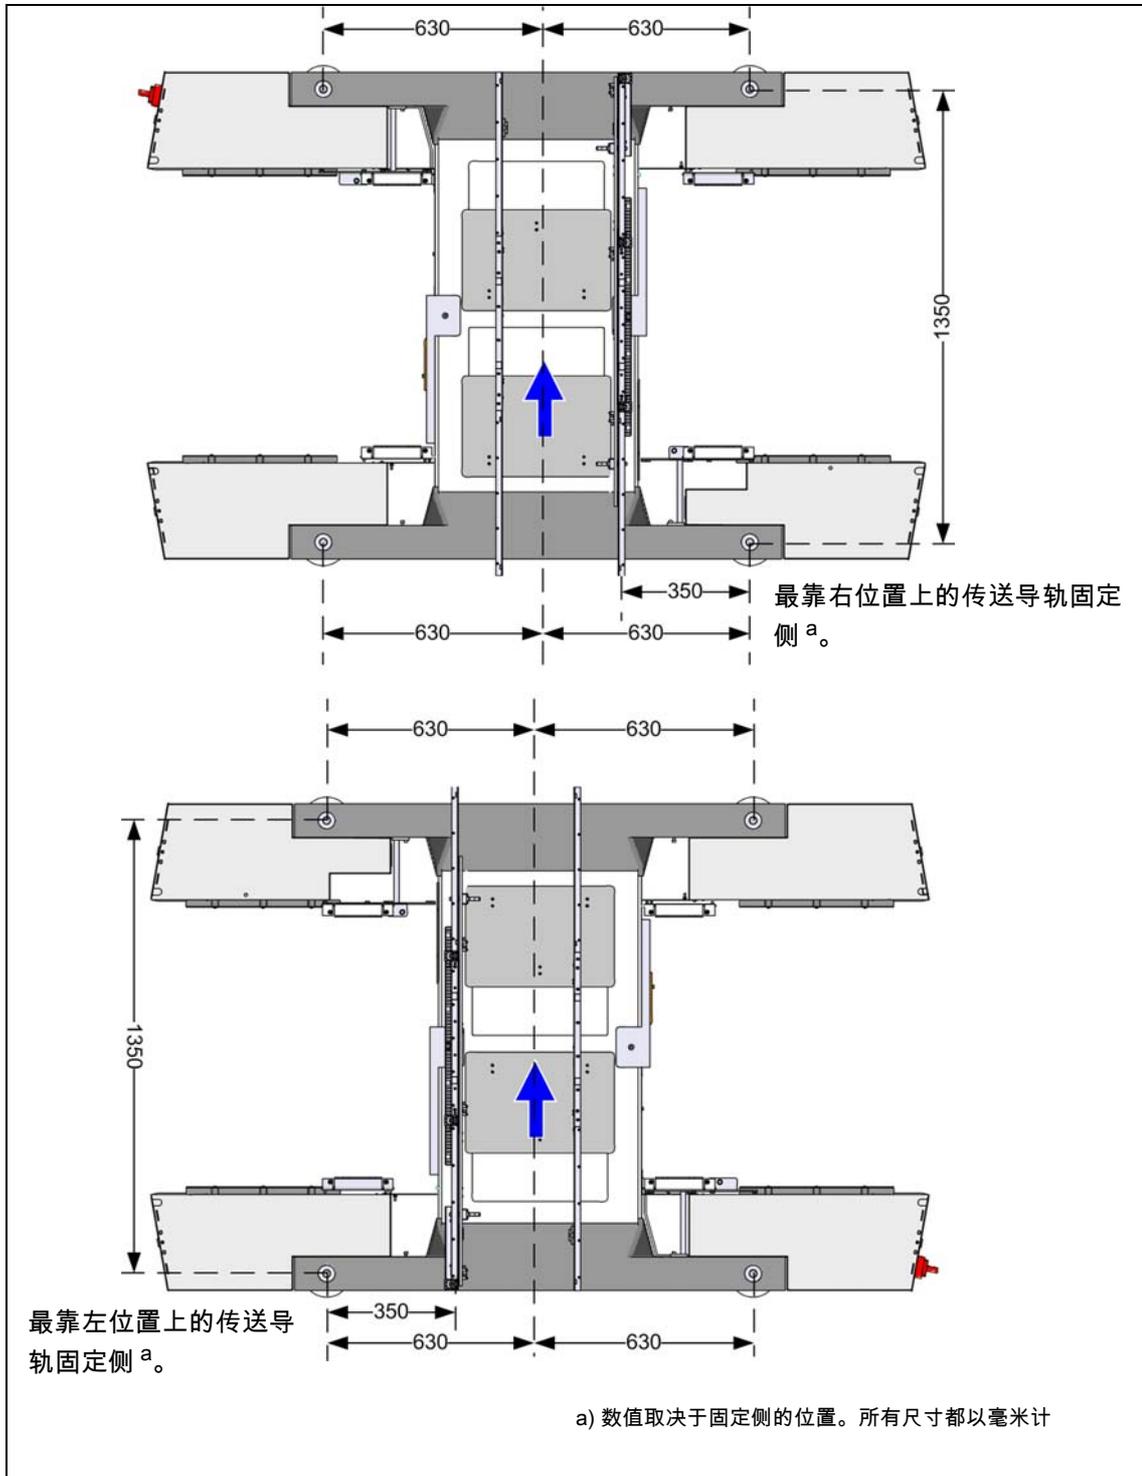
4 PCB 单传送导轨的贴片机支脚间隙 (以毫米为单位)
